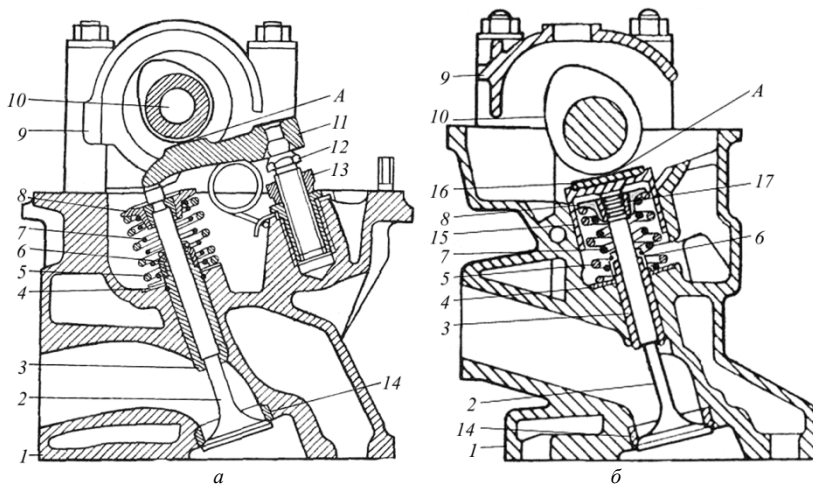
Расположение деталей клапанной группы ГРМ с рычажным приводом (а) и с цилиндрическим толкателем (б): 1 – головка цилиндров; 2 – клапан; 3 – направляющая втулка клапана; 4 – опорная шайба; 5 – пружина клапана внешняя (большая); 6 – сальник клапана; 7 – пружина клапана внутренняя (малая); 8 – тарелка пружин клапана; 9 – корпус подшипников распределительного вала; 10 – распределительный вал; 11 – рычаг клапана; 12 – упорный винт; 13 – контргайка; 14 – седло клапана; 15 – цилиндрический толкатель; 16 – регулировочная шайба; 17 – сухарь; A – регулируемый тепловой зазор
